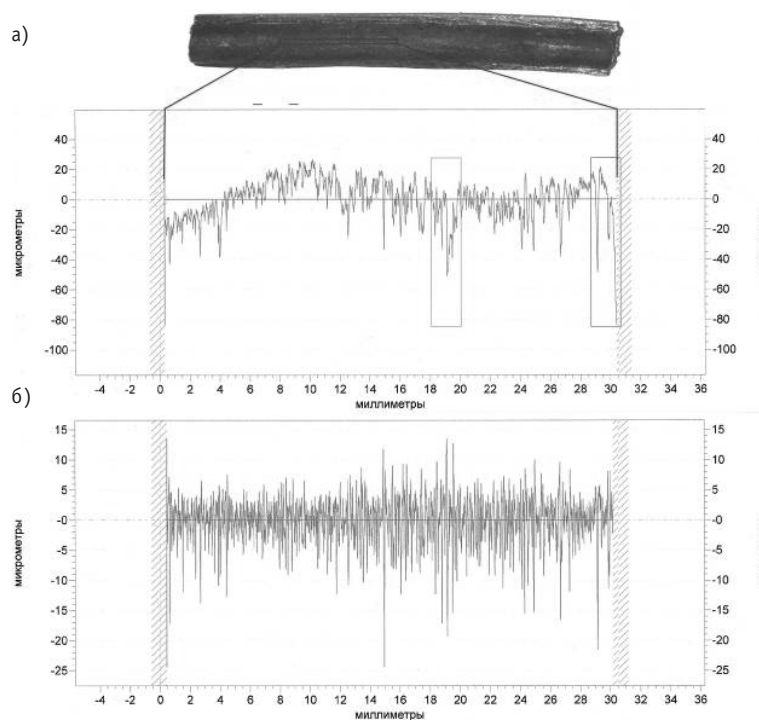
Профилограмма (профиль а) и шероховатость (б)) поверхности свинцовой пробки образца 4
